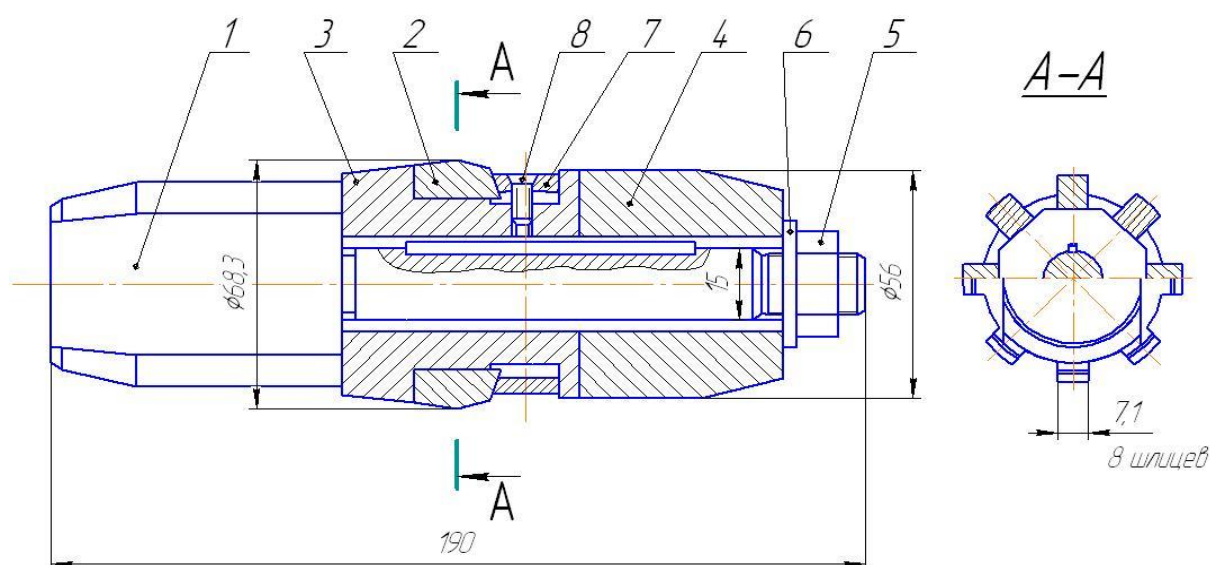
Фасонный дорн для калибровки шлицевых отверстий: 1-оправка, 2-твердосплавные пластины, 3-корпус, 4-втулка, 5-гайка, 6-шайба, 7-сухарик, 8-винт
